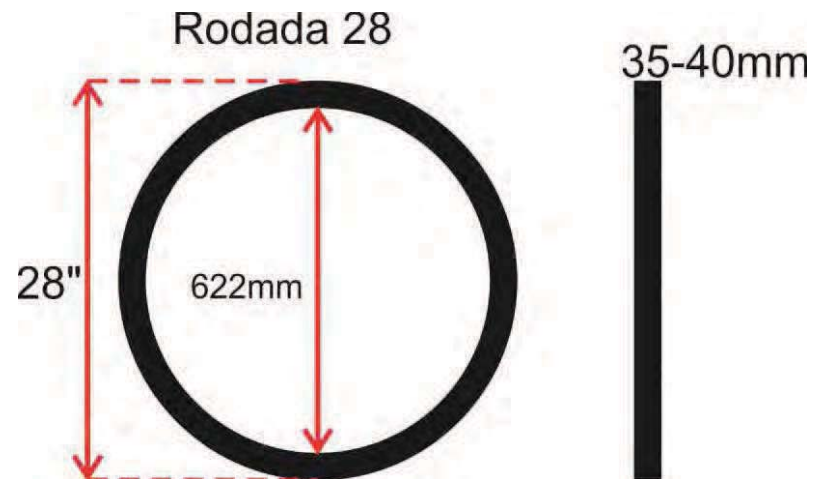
/Medidas de llanta más utilizadas para bicicleta híbrida.
